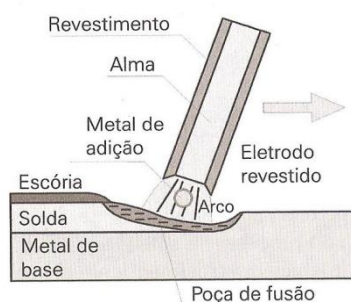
Esquema de uma soldagem com eletrodo revestido.
